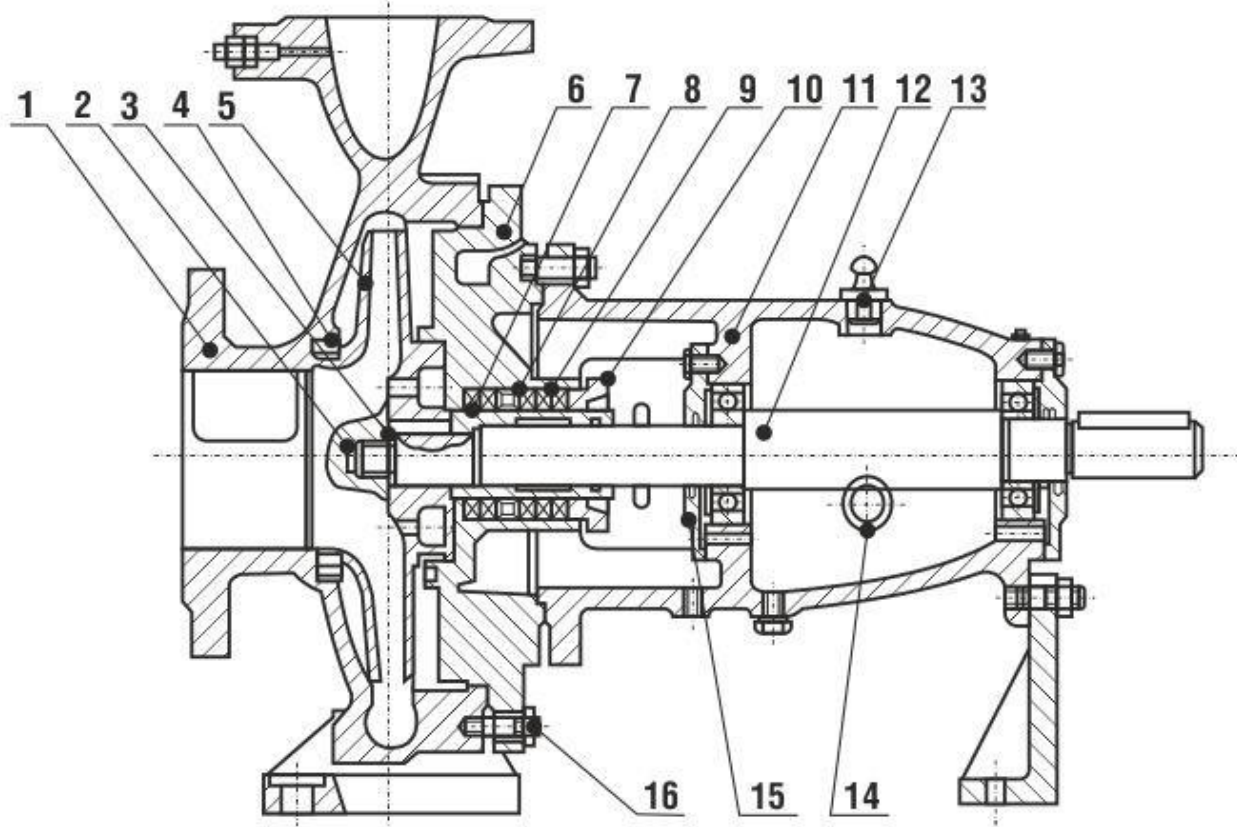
Центробежный насос К80-50-200: 1 – корпус насоса; 2 – гайка рабочего колеса; 3 – шпонка; 4 – кольцо уплотнительное; 5 – рабочее колесо; 6 – крышка корпуса; 7 – защитная втулка; 8 – кольцо сальника; 9 – сальниковая набивка; 10 – фланец уплотнения; 11 – кронштейн; 12 – вал; 13 – пробка для заливки масла; 14 – контрольное окно; 15 – крышка подшипников; 16 – шпилька с гайкой
